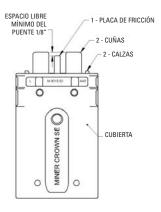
Corona SE/SG Inspección Fuera del Carro
